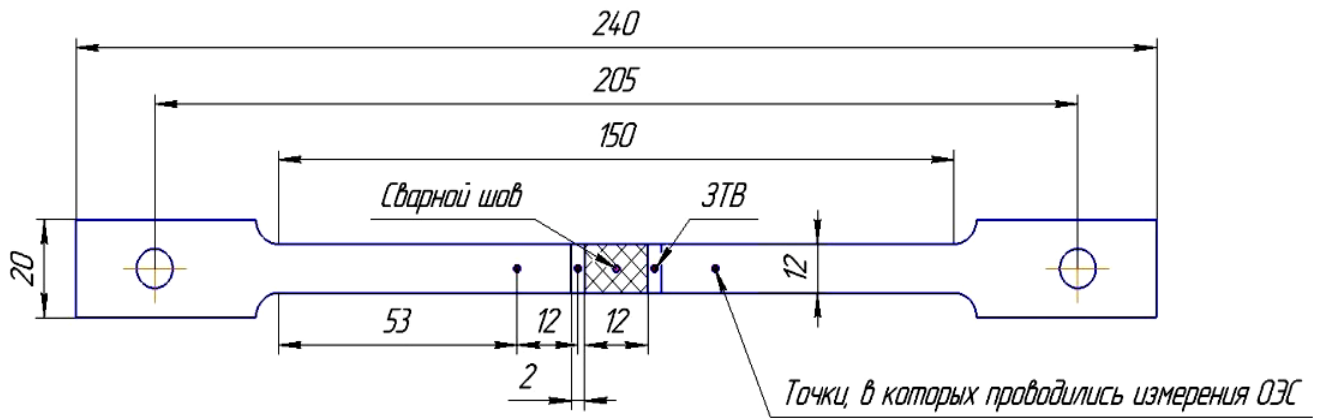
Эскиз образцов из стали 09Г2С со сварным соединением
